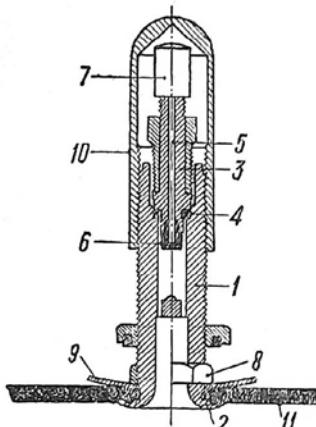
Вентиль с игольчатым клапаном: 1 – корпус вентиля, 2 – пята вентиля, 3 – золотник, 4 – резиновая шайба, 5 – шток клапана, 6 – резиновый конус, 7 – головка клапана, 8 – гайка, 9 – шайба, 10 – пыльный колпачок
